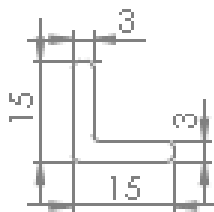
Vista frontal da caixa do banco de baterias traseiro – corte
